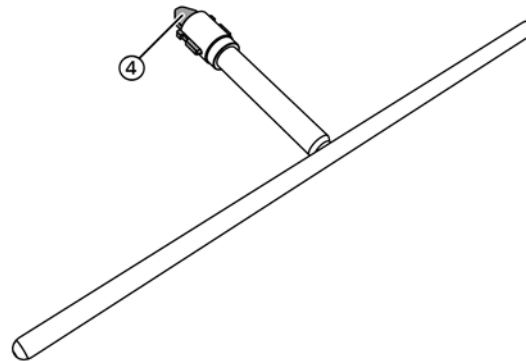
Приводной рычаг заземляющего выключателя сборной шины (принципиальная схема)
